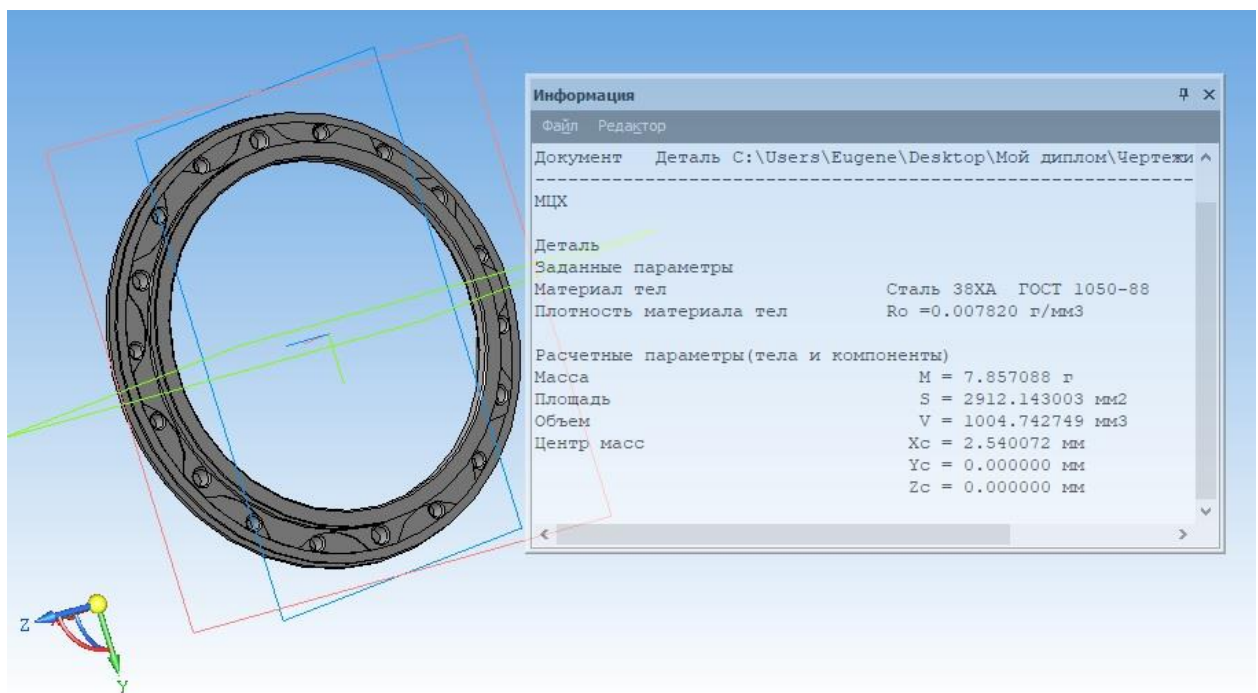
3D модель деталі «Поршень» з вагою.
